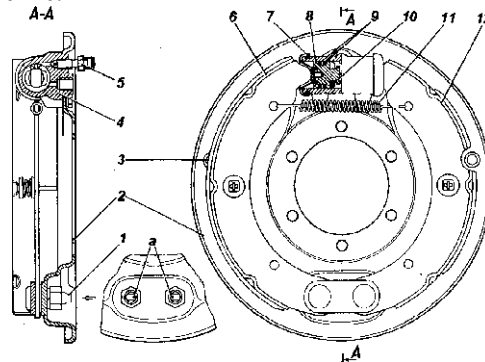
Тормоз заднего колеса: а -метки на опорных пальцах; 1 -опорные пальцы; 2 -щит; 3 -отверстия для визуального контроля состояния тормозных накладок; 4 -колесный тормозной цилиндр; 5 -перепускной клапан; 6,12 -тормозные колодки; 7 -защитный колпак; 8 -поршень; 9 -уплотнительные кольца; 10 -упорное кольцо; 11 -стяжная пружина
